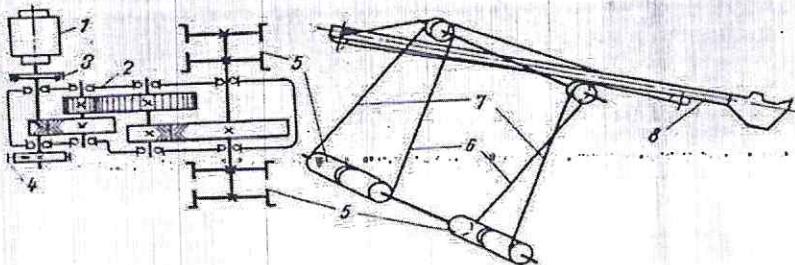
Mecanism de impingere cu cablu: 1) motor electric; 2) reductor; 3) cuplaj de moment maxim; 4) frina; 5) tambur; 6) cablu de impingere; 7) cablu de retragere; 8) miner.
